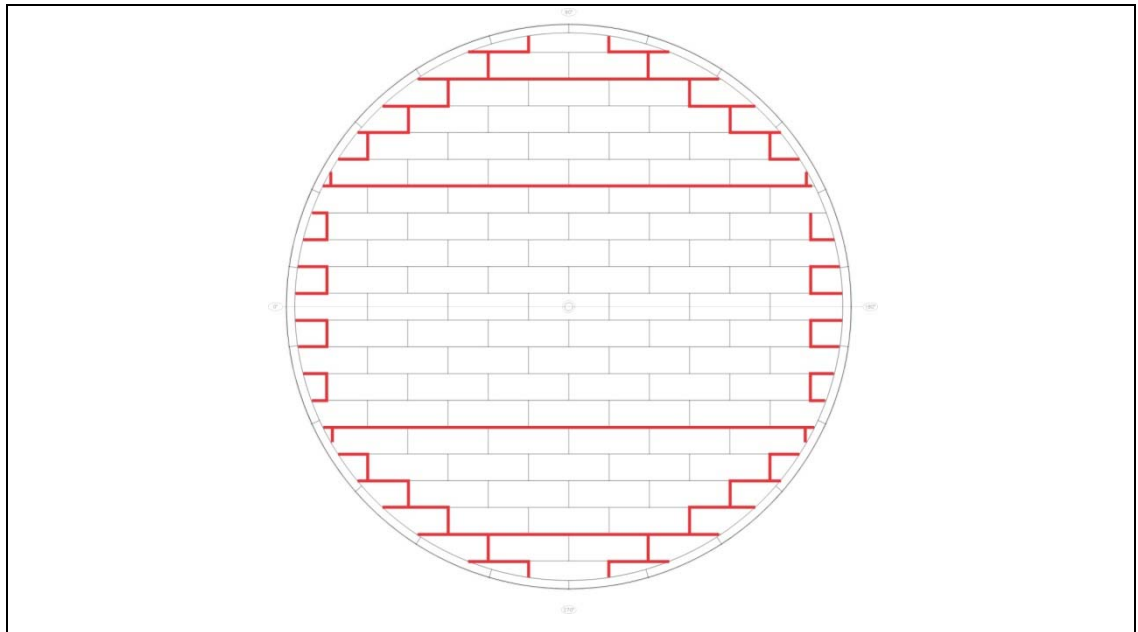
Juntas que serão soldadas por último. Autores
